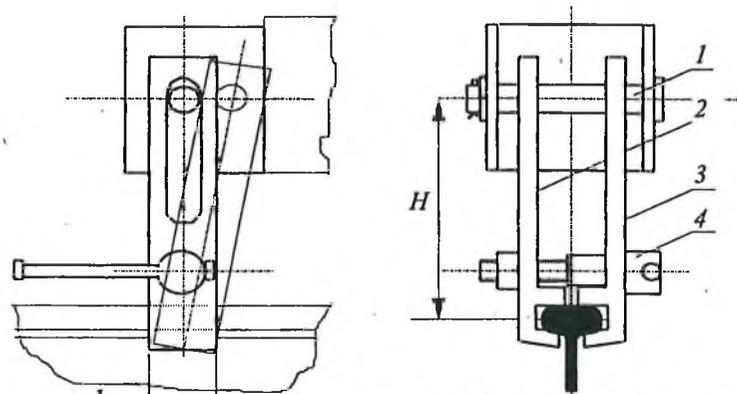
Схема самозаклинивающегося ручного противоугонного захвата
